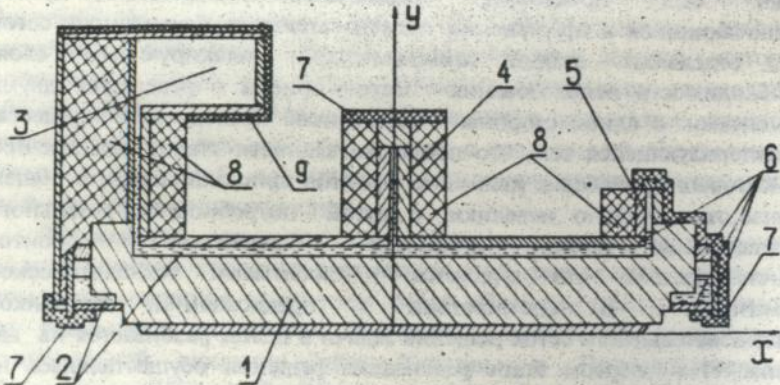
Общий вид скользящей опоры шагающего экскаватора с предлагаемой теплоизоляцией конструкции и модифицированной технологической оснасткой под плакирование: 1 - стальная основа изделия; 2 - наплавочные полости; 3 - коробчатый бункер; 4 - промежуточный питатель; 5 - питатель-газосборник; 6 - контрдетали; 7 - шестислойная изоляция из асбокартона; 8 - изоляция из асброкши; 9 - четырехслойная изоляция из асбокартона.
